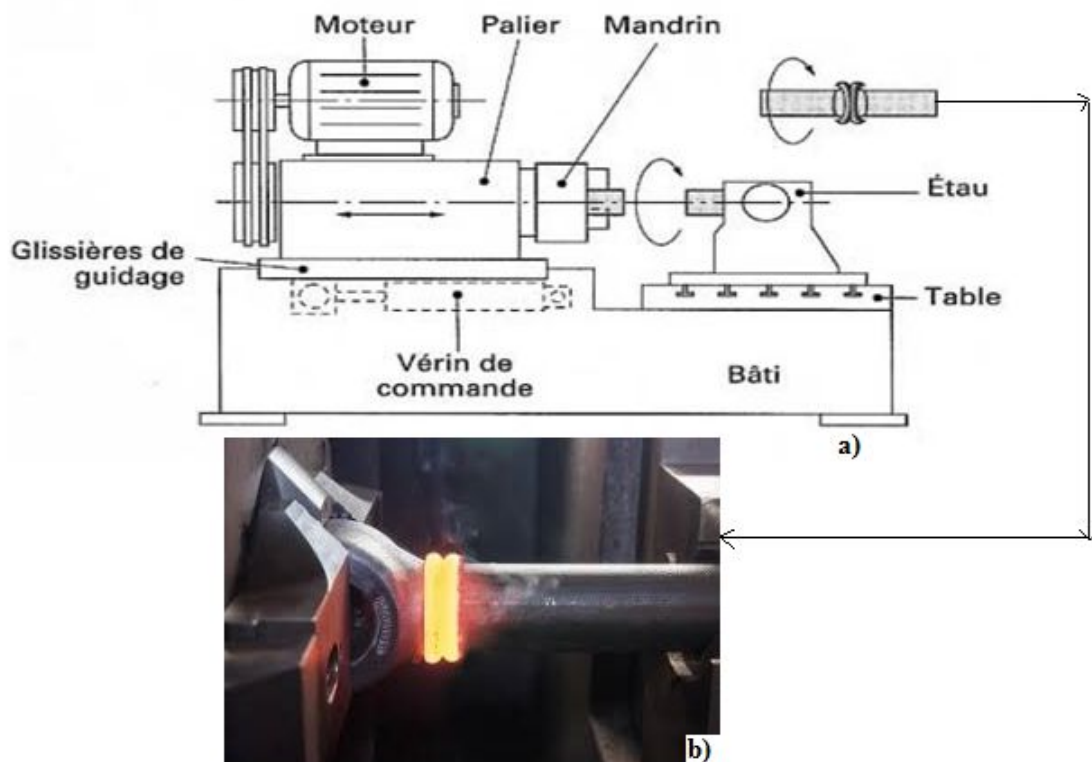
Soudage par friction ; a) schéma d'une machine de soudage par friction, b) exemple de soudage pour la fabrication des vérins hydraulique [2].
